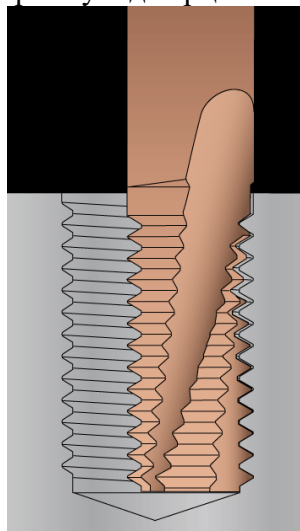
Схема різбофрезерування інструментом зі зворотною конусністю
